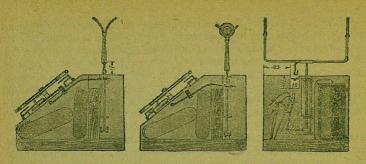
Слева — трубка снята с рычага; стопорный зуб удерживает зубчатый диск ползунка. В середине — трубка положена на рычаг; стопорный зуб освободил диск ползунка. Справа — место и размеры выреза для рычага стопорного зуба в вертикальной панели аппарата.
